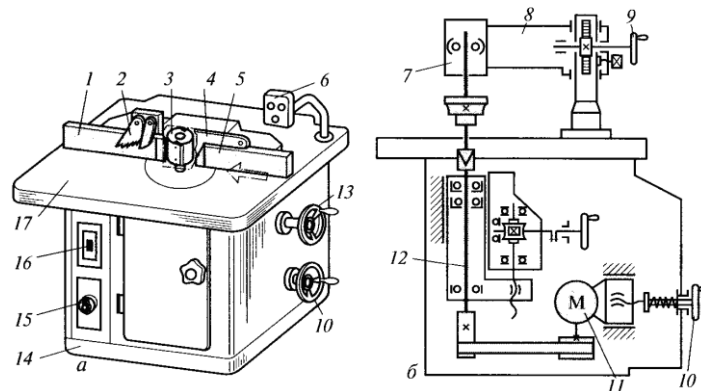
Фрезерний верстат з ручною подачею: а – загальний вигляд; б – кінематична схема; 1, 5 – напрямні лінійки; 2 – зубчастий сектор; 3 – різальний інструмент (фреза); 4 – огороження; 6 – пульт керування; 7 – додаткова опора шпинделя; 8 – кронштейн; 9 – маховичок підйому кронштейна; 10 – маховичок натягу ремня; 11 – електродвигун; 12 – шпиндель; 13 – маховичок настроювання шпинделя по висоті; 14 – станина; 15 – перемикач частоти обертання шпинделя; 16 – вимикач; 17 – стіл
